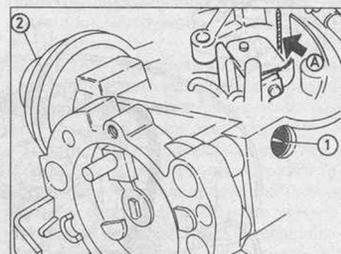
Проверка зазора воздушной заслонки (Глава 16)
